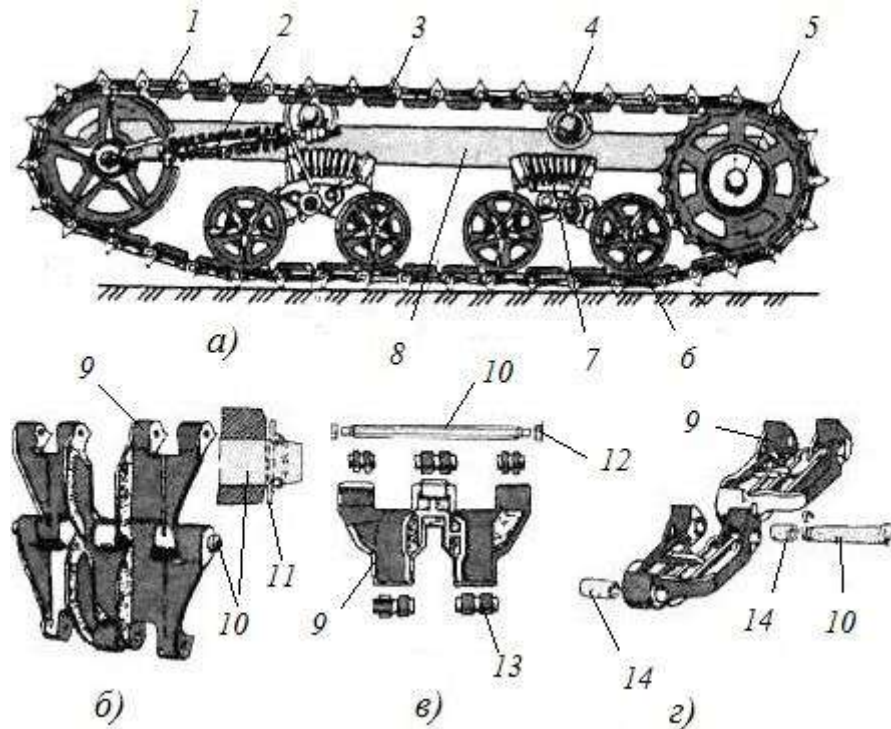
Гусеничні рушії: а – еластична підвіска; б, в, г – типи гусениць; 1 – напрямляюче колесо; 2 – механізм натягування і амортизації; 3 – гусениця; 4 – підтримуючий ролик; 5 – ведуче колесо; 6 – опорний коток; 7 – пружина (амортизатор); 8 – рама; 9 – траки (ланки гусениці); 10 – палець; 11 – штопорне кільце; 12 – гайка; 13 – гумометалева втулка (шарнір); 14 – металева втулка
